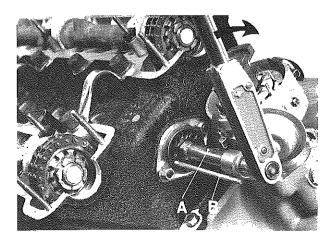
A) Dado cieco n. 23 - B) Estrattore n. 24 A) Cap nut No. 23 - B) Tool No. 24
